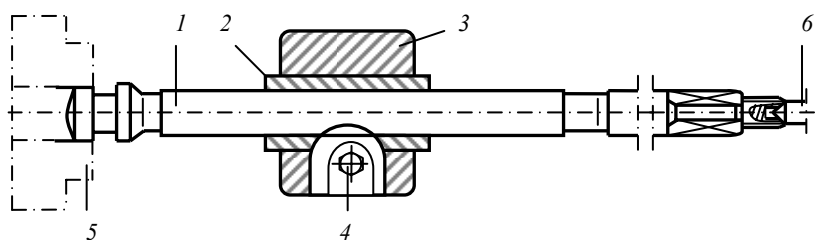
Устройство для шлифования уплотнительной поверхности шпинделя:
